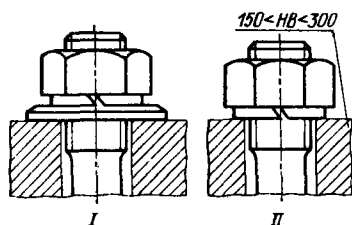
Установка шайб Гровера с учетом твердости поверхностей
